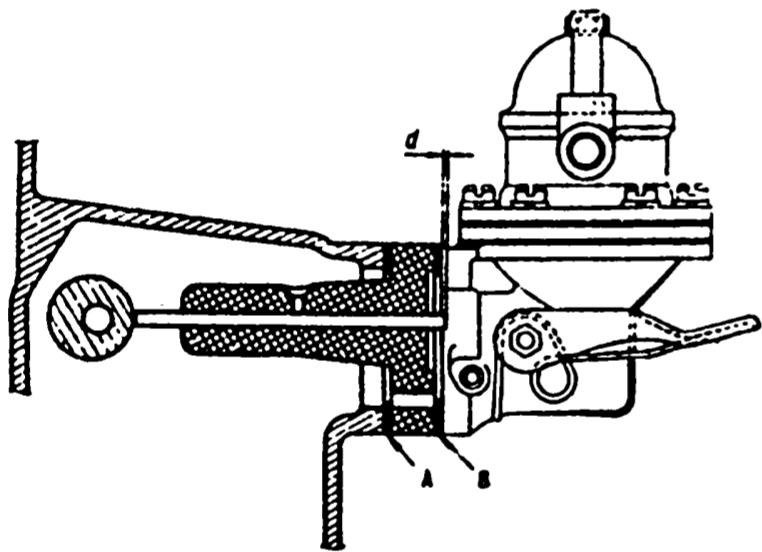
Схема контроля и регулировки выступающего толкателя привода насоса: А - прокладка толщиной 0,27 - 0,33 мм; В - прокладка толщиной 0,70 - 0,80 мм; d - выступание толкателя
